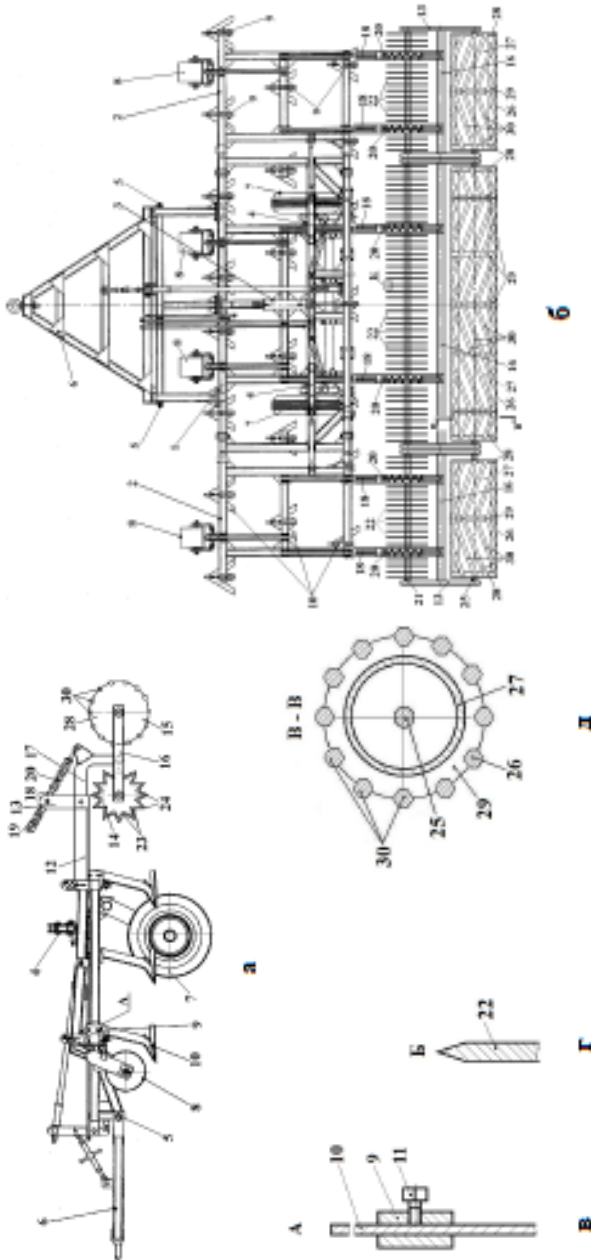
Агрегат для поверхностной обработки почвы (обозначения в тексте): а – вид сбоку, б – вид сверху, в – сечение держателя рабочего органа, г – поперечное сечение заточенной вершины дискового рыхлителя, д – поперечное сечение катка выравнивающего типа, 1, 2 – центральная и боковая секции соответственно; 3, 4 – механизм перевода; 5 – палец; 6 – снац; 7, 8 – транспортные и опорные колеса соответственно; 9 – держатель; 10 – рабочие органы; 11 – болт; 12 – балка; 13 – катковые приставки; 14, 15 – каток рыхлительного и выравнивающего типа соответственно; 16 – H-образная рама; 17 – кронштейн; 18 – штанга; 19 – гайка; 20 – пружина; 21 – ось; 22 – Дисковые рыхлители; 23 – треугольные выемки; 24 – заточенная вершина; 25 – ось; 26, 27 – наружный и внутренний барабаны; 28, 29 – боковые и промежуточные Диски соответственно; 30 – пружок
